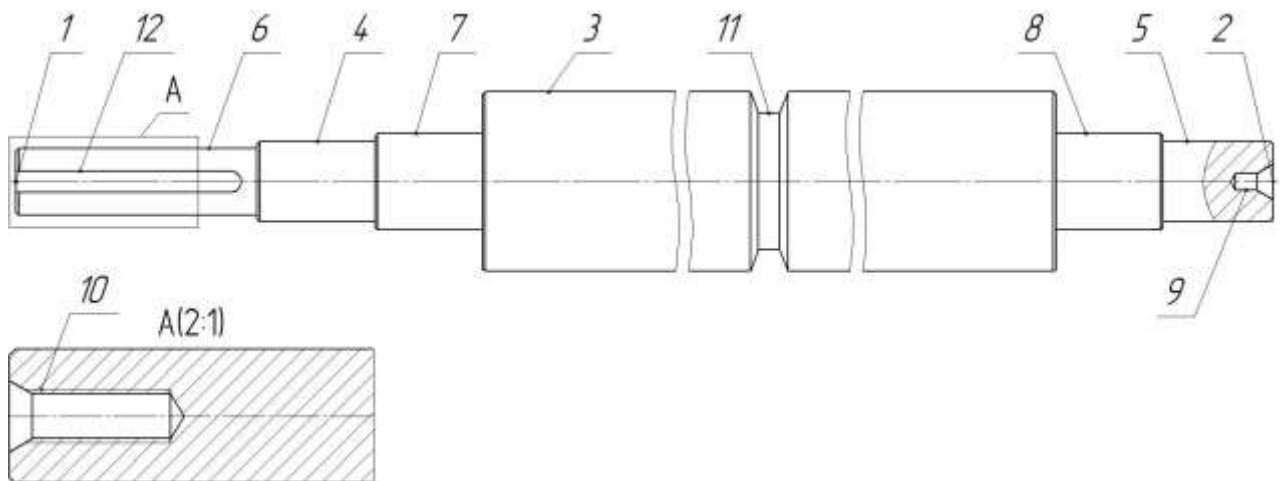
Поверхні, що обробляються в деталі вал привідний
